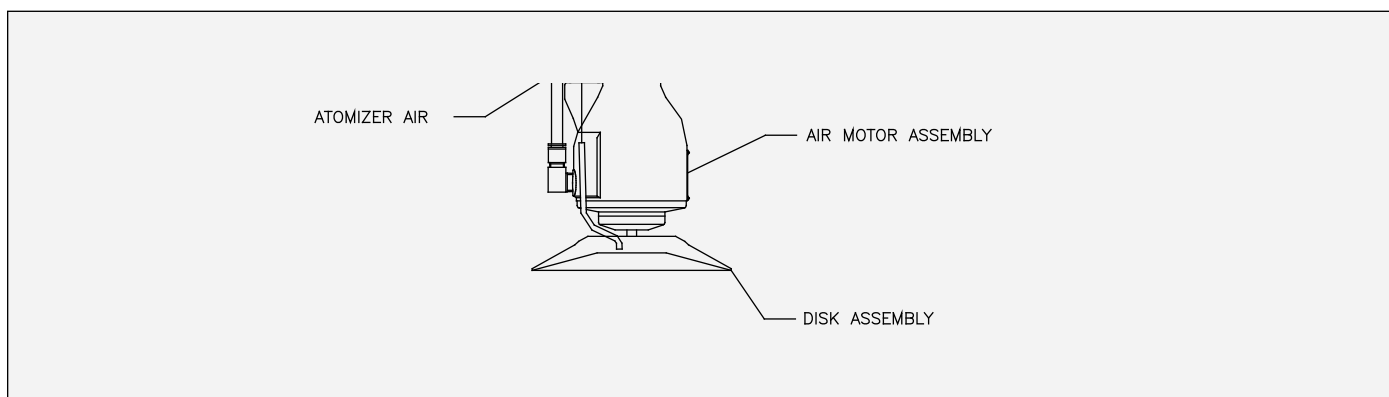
Шланг в сборе для сжатого воздуха 78166-00
